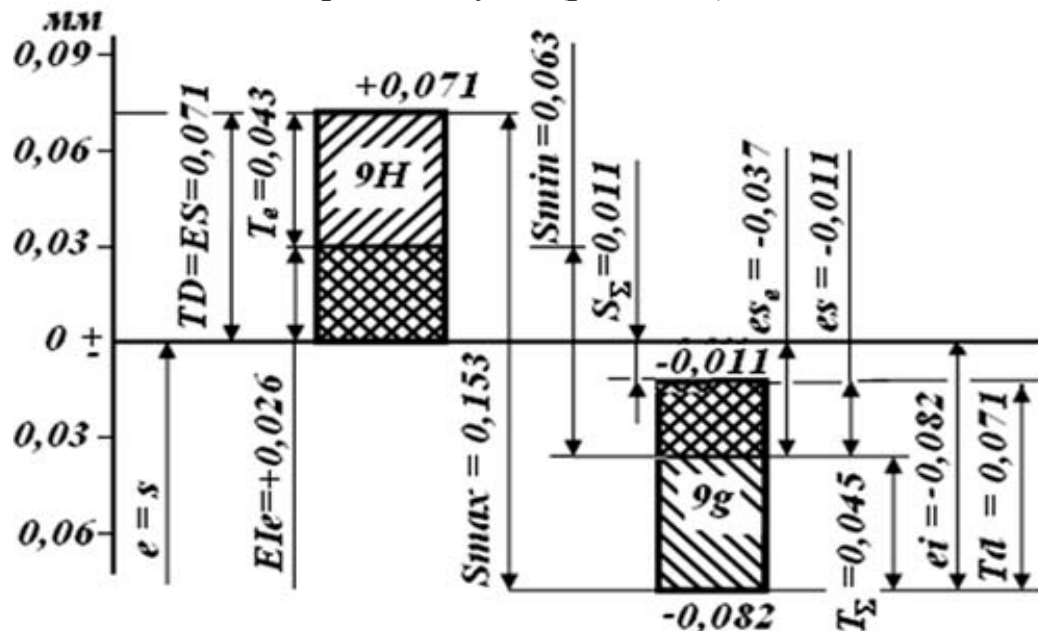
Схема розташування полів допусків за бічними поверхнями зубів:
